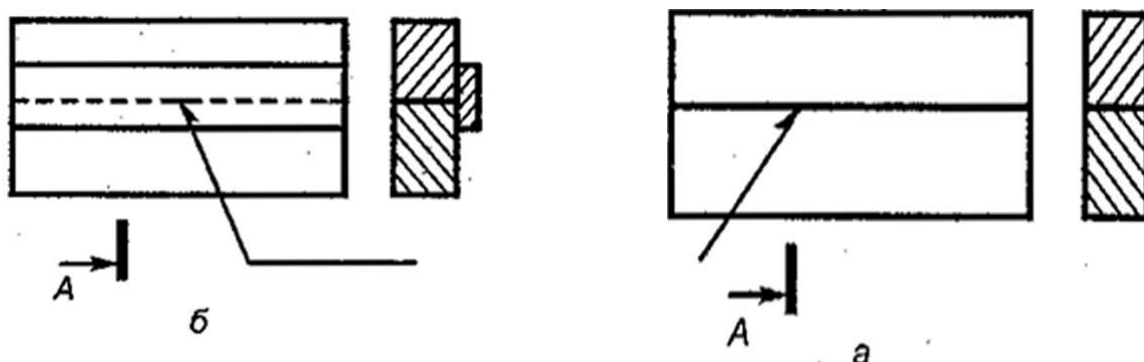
Обозначения видимого и невидимого шва сварного соединения
